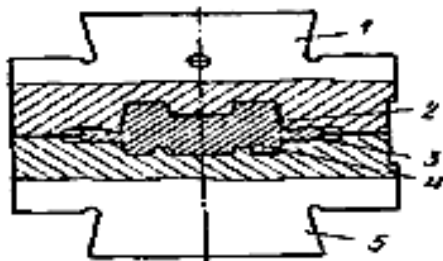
Цельноблочный штамп: 1 – верхний штамп; 2 – ручей; 3 – заусенец; 4 – нагретая заготовка; 5 – нижняя часть штампа.
